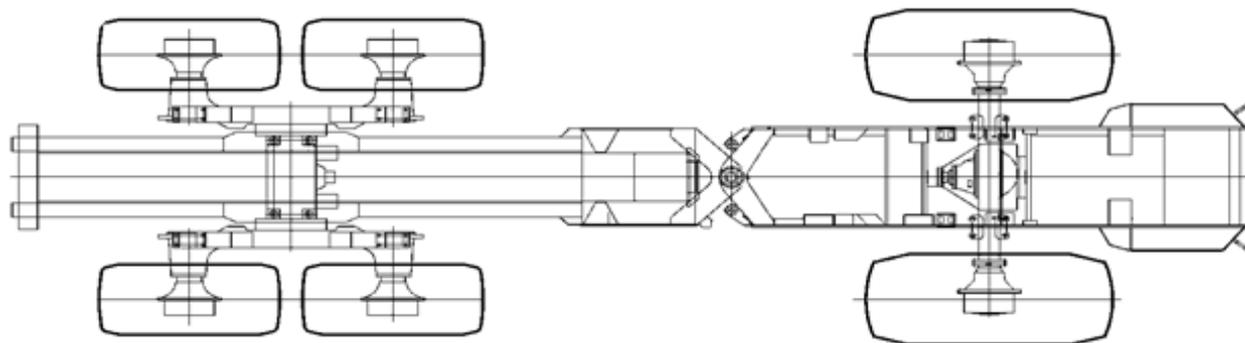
Подвеска задних колес форвардера АМКОДОР 2661
